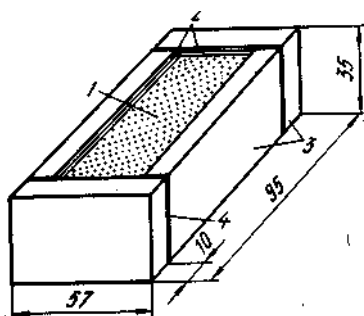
Шамотная форма для изготовления образцов из фосфатного огнеупорного раствора:
